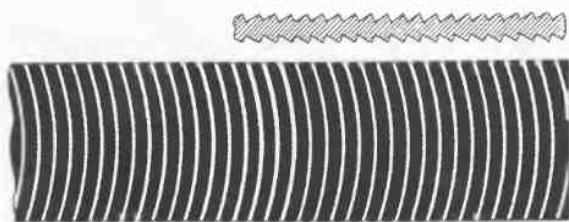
Напильник с фрезерованными зубьями (шаг зуба около 3 мм) для обработки мягких материалов (продольный разрез и вид сверху конца напильника)
